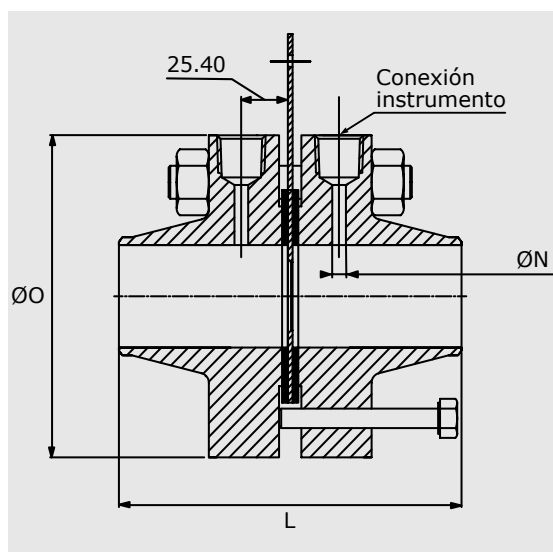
Dimensiones generales de conjunto para Flange Tap y brida WN.
